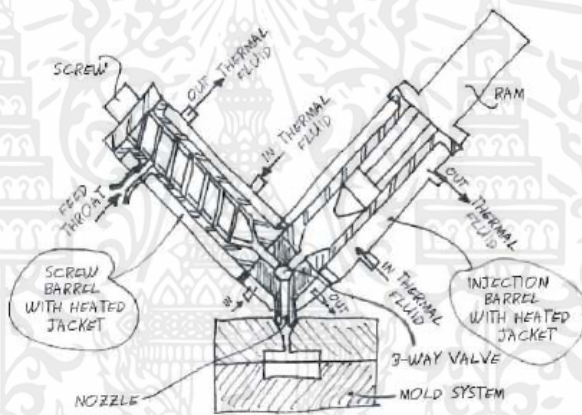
เครื่องจักรแม่พิมพ์แบบฉีดแนวตั้ง (Vertical Injection molding machine)
